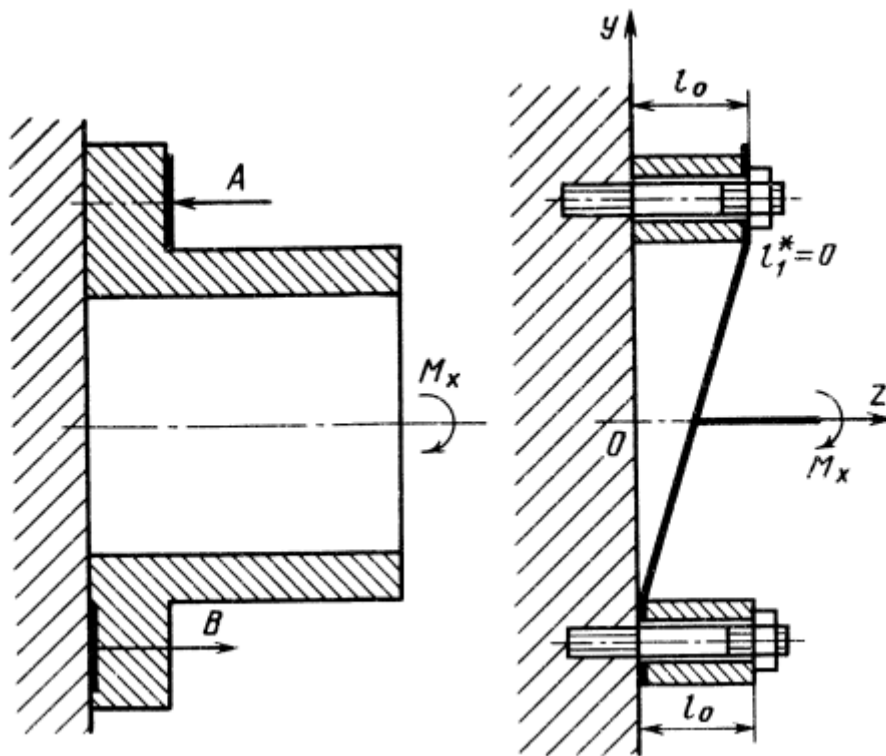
Расчетная схема соединения, работающего на изгиб.
